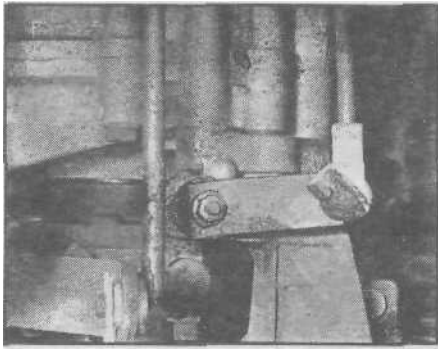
Тяги штанги выбора передач и пластмассовый шаровой шарнир
